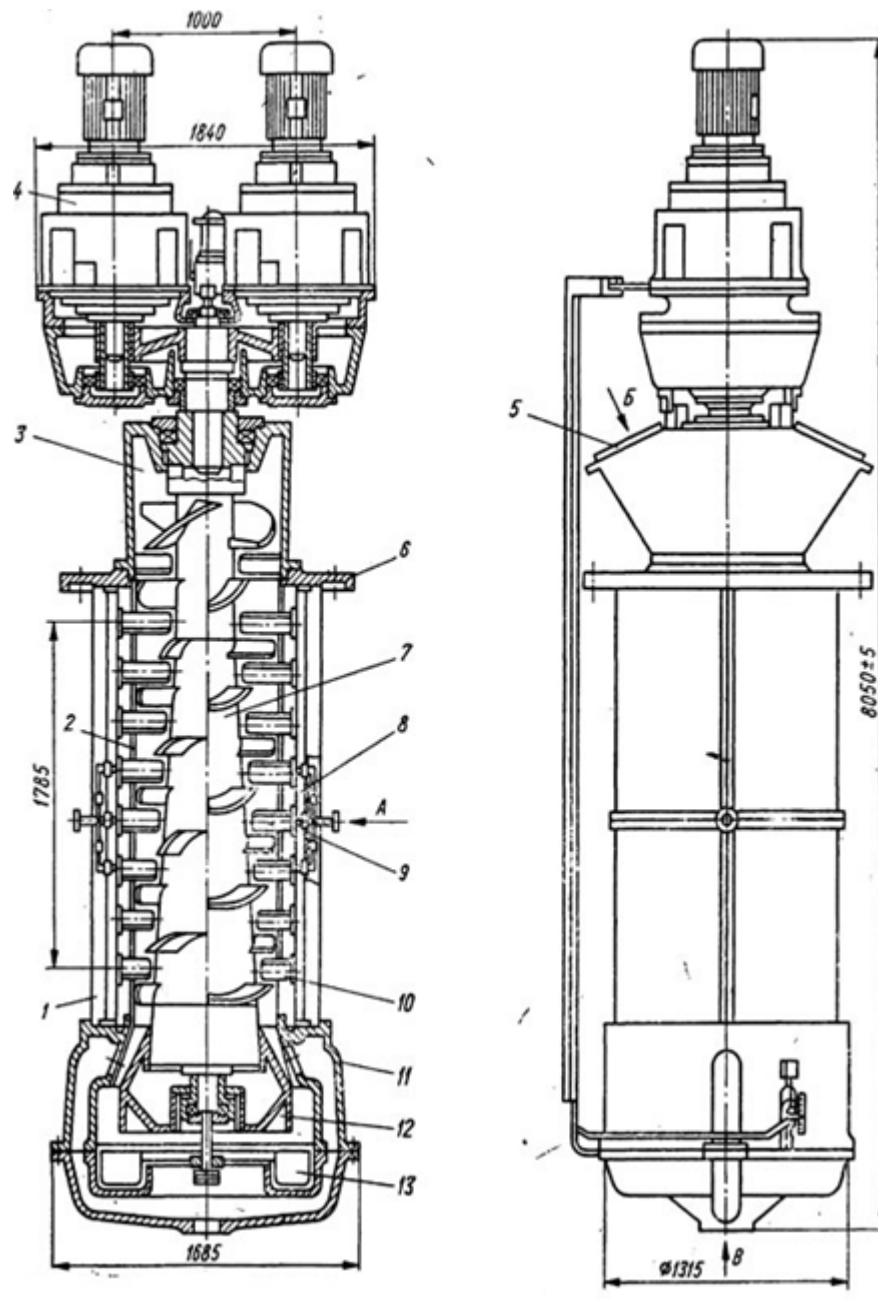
Вертикальний жомовий прес А2-ППВ
